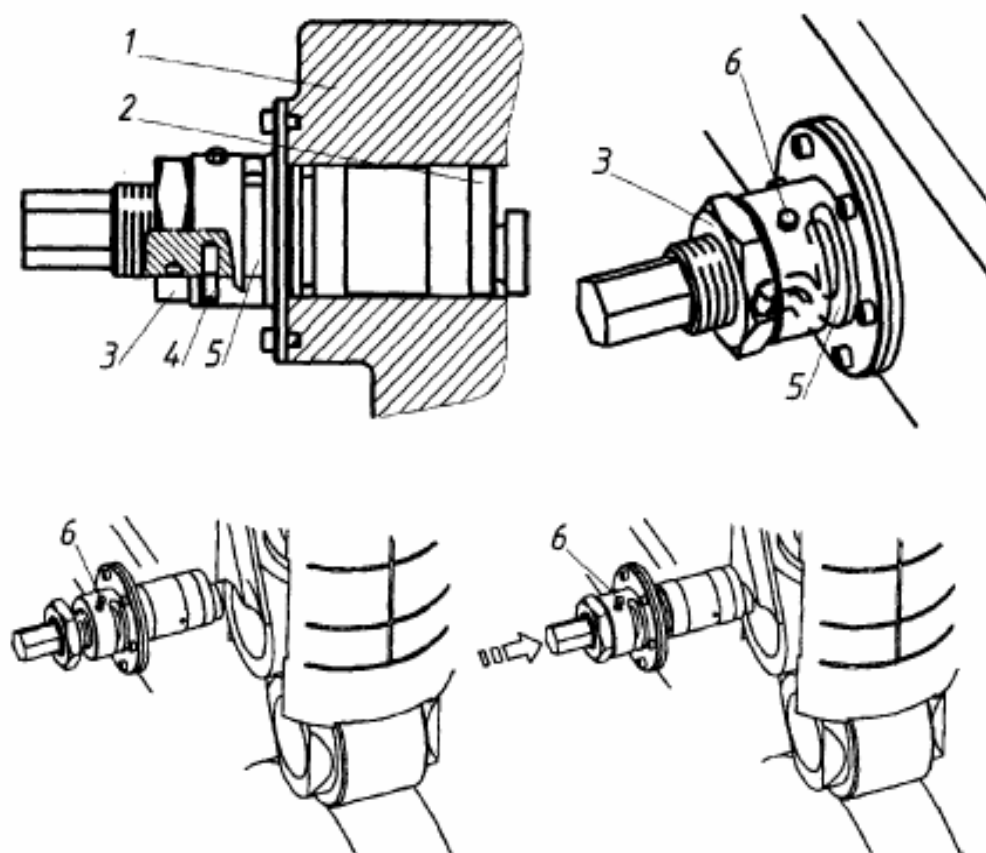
Підйомне і фіксувальне облаштування штовхальника ПНВТ дизеля серії МС фірми MAN ексцентрикового типу: 1 - корпус штовхальника; 2 - ексцентриковий підйомник; 3 - контргайка; 4 - направляючий штифт; 5 - канавка напрямляючої; 6 - стопорний гвинт.
